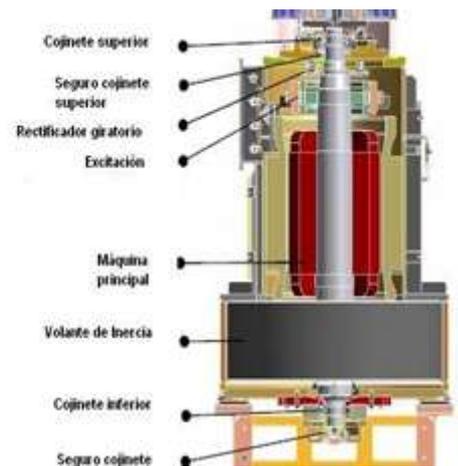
Esquema de volante de inercia con rodamiento magnético. Fuente: [2].
